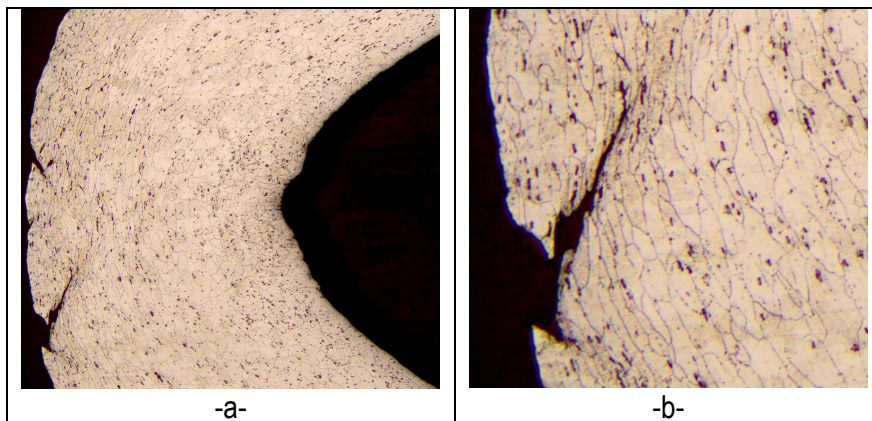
Fissuration de la tôle en fin d'essai de pliage.
